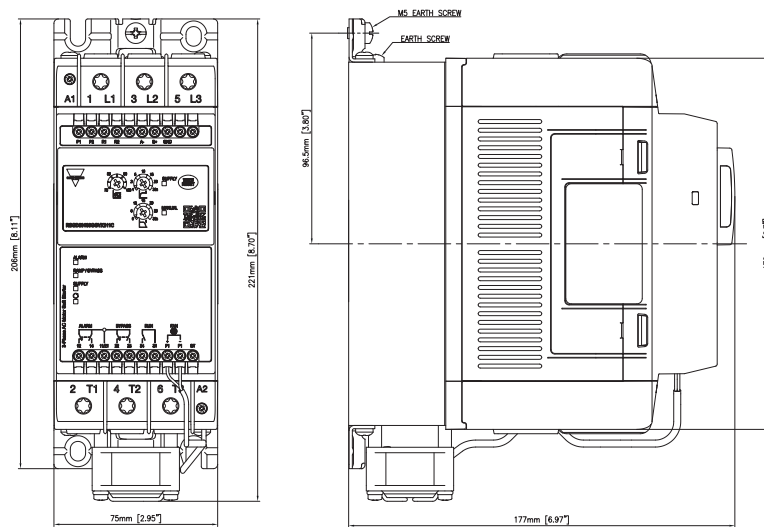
RSGD..100..VX311C (versione per montaggio a pannello)
